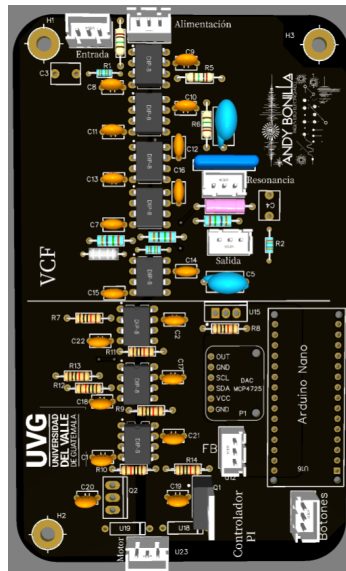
Vista 3D de PCB filtro controlado por voltaje
